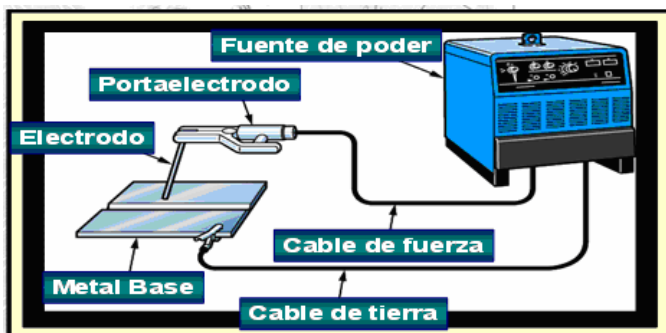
Equipo básico de soldadura SMAW.
